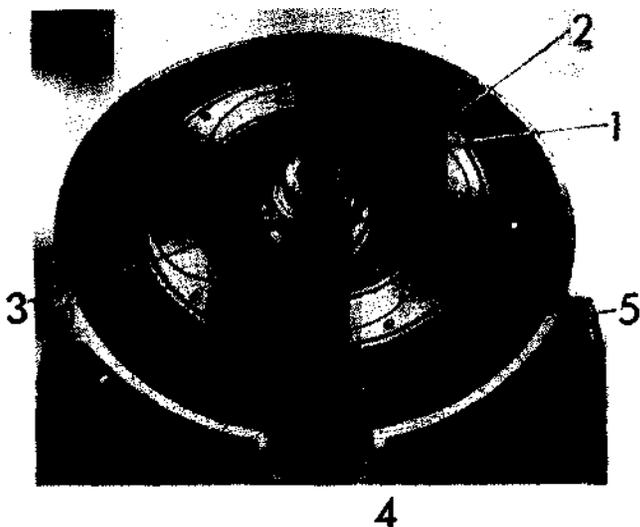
Sistema de engrase en la superficie de guía del banco; 1, guía con ranuras de engrase; 2, tubos de comunicación del aceite; 3, rodamiento de centraje; 4, piñón de ataque (cónico); 5, banco.
